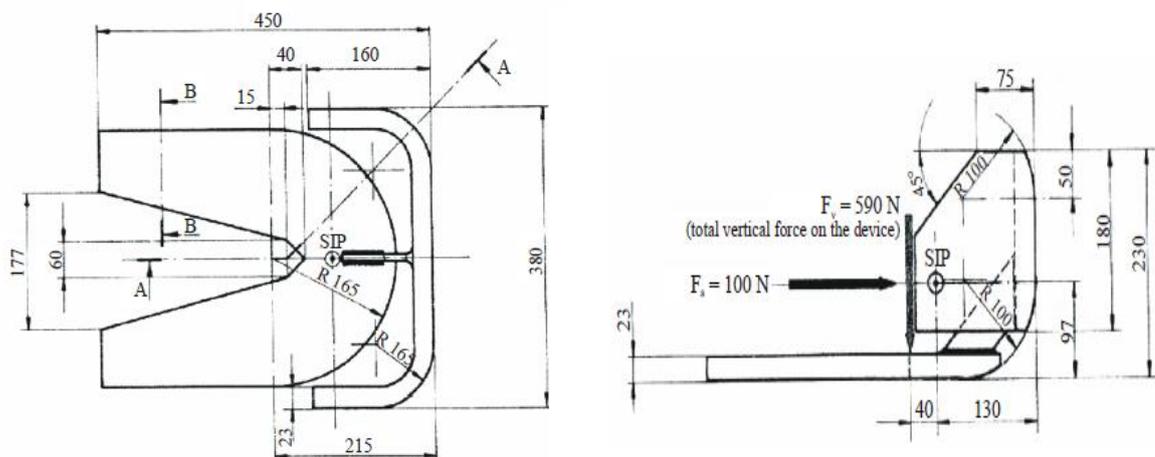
Detalhamento construtivo do dispositivo para determinação do SIP em vistas superior e lateral.
